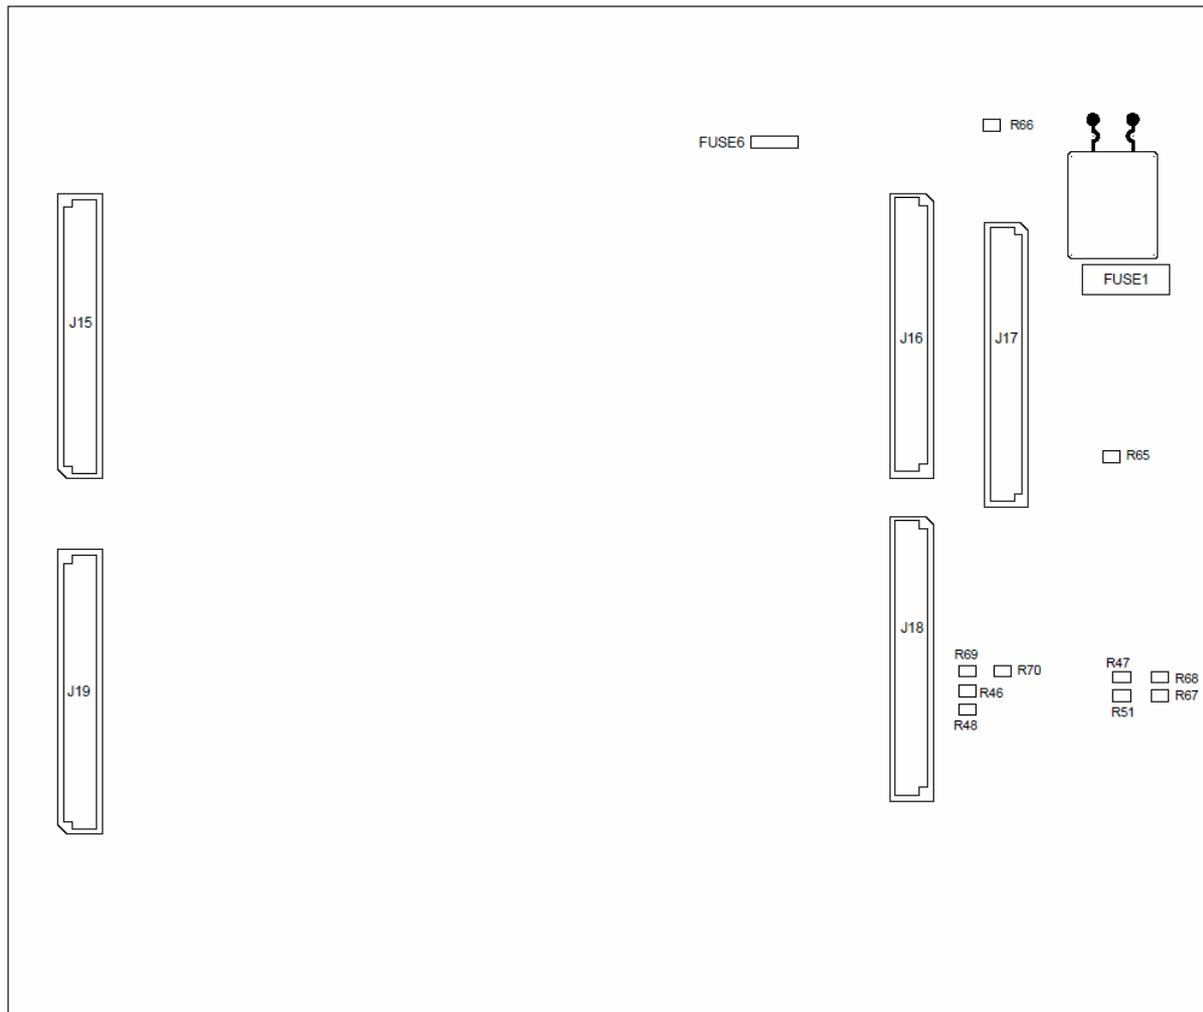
Layout lato saldature di connettori, ponticelli e fusibili
